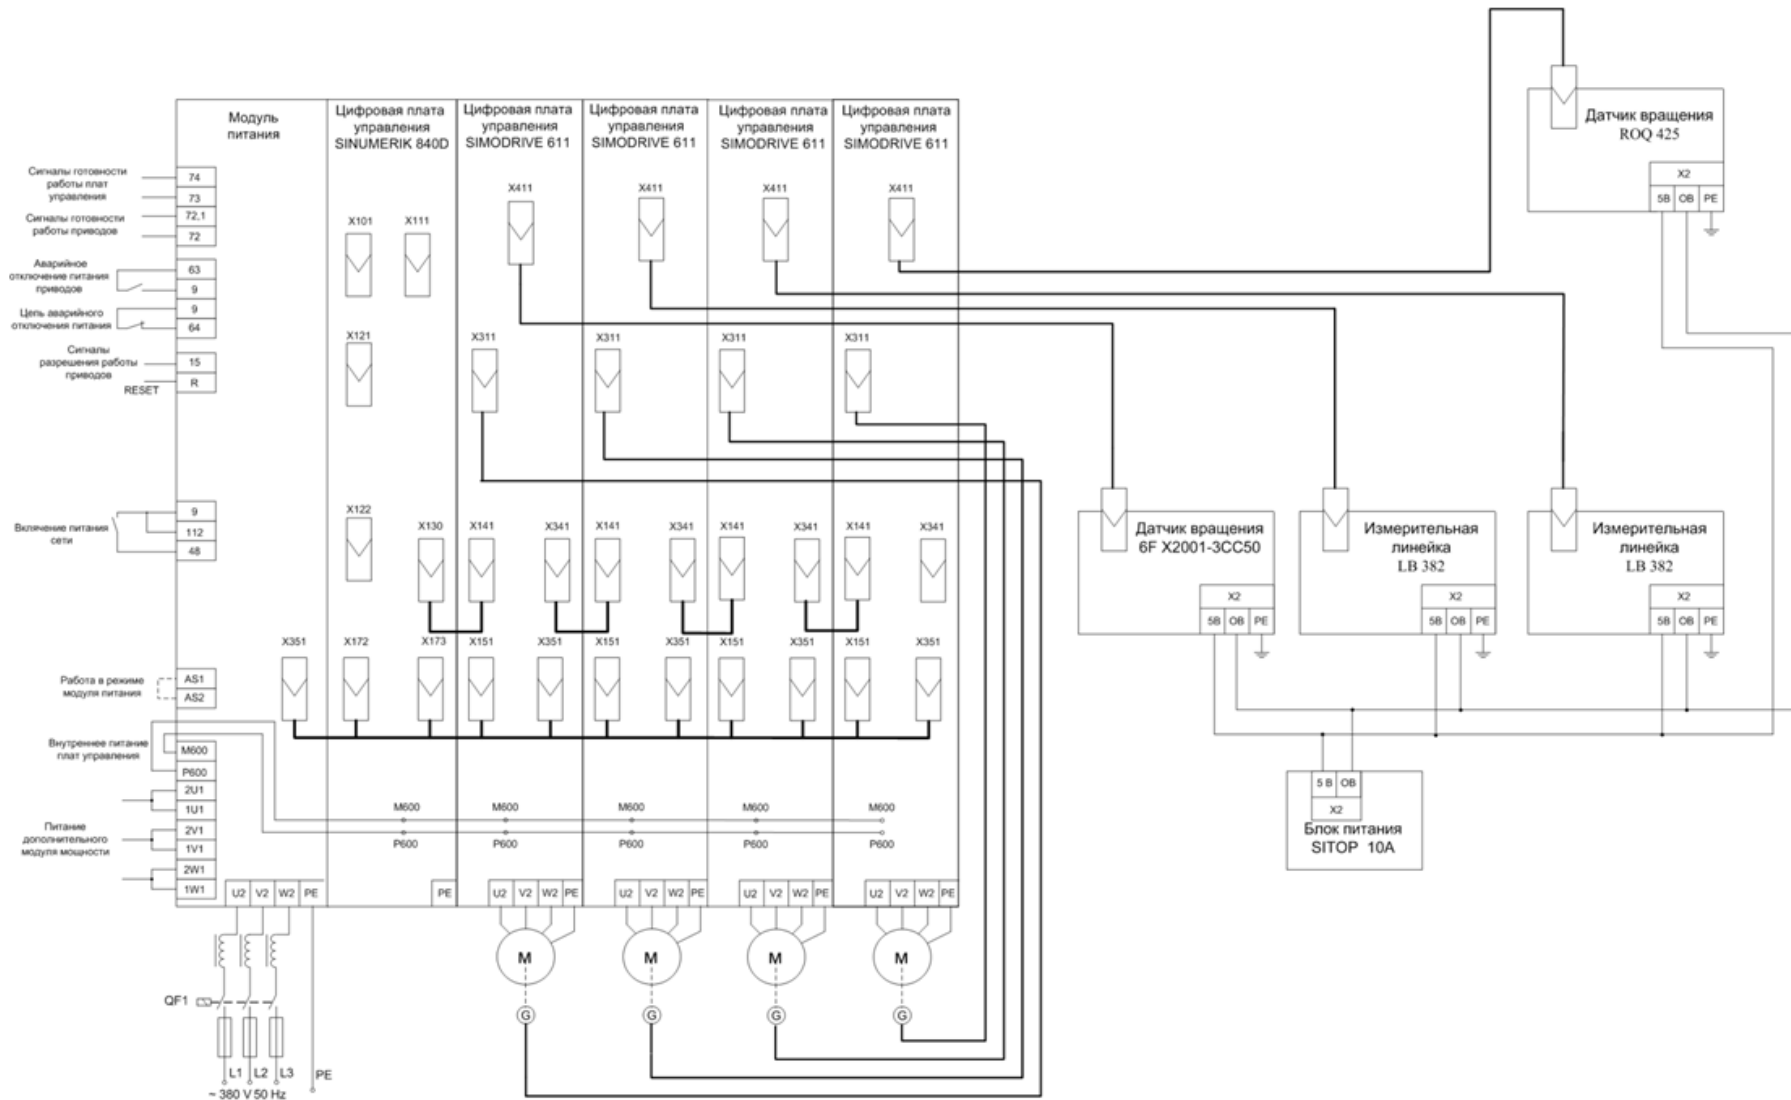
Приводна система SINUMERIK 840D для фрезерного верстата із ЧПУ
